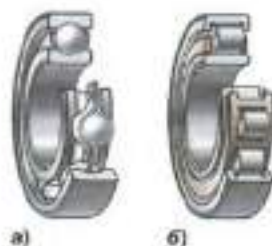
Различные виды подшипников: а — шариковый; б — роликовый
